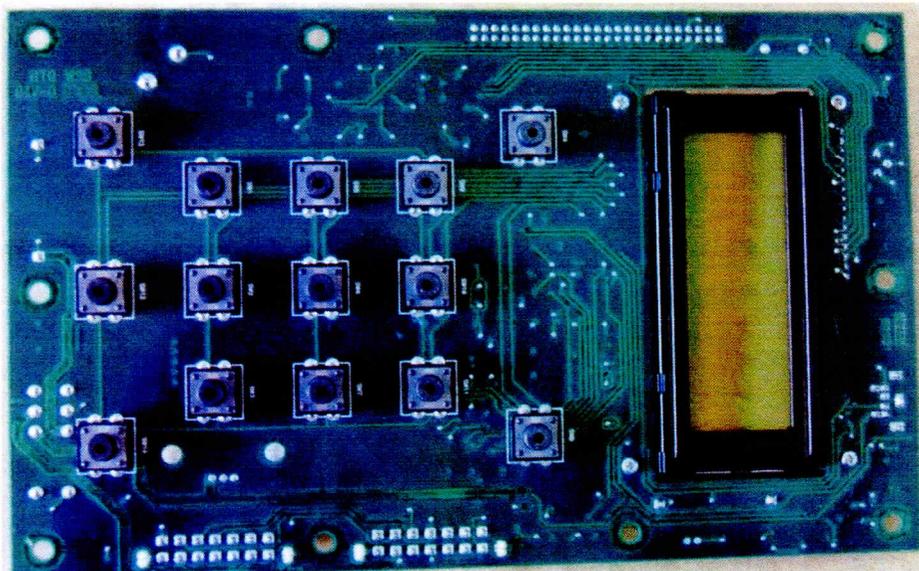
Tarjeta LOCAL PRESET identificada con número de parte 110792 revisión A vista cara de soldadura.
